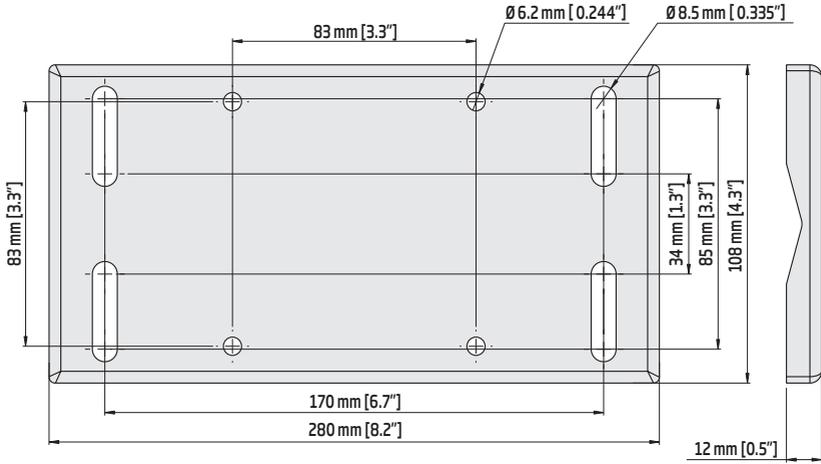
Grosor del Panel de Montaje en Pared, Dimensiones de los Pernos de Montaje y las Ranuras
